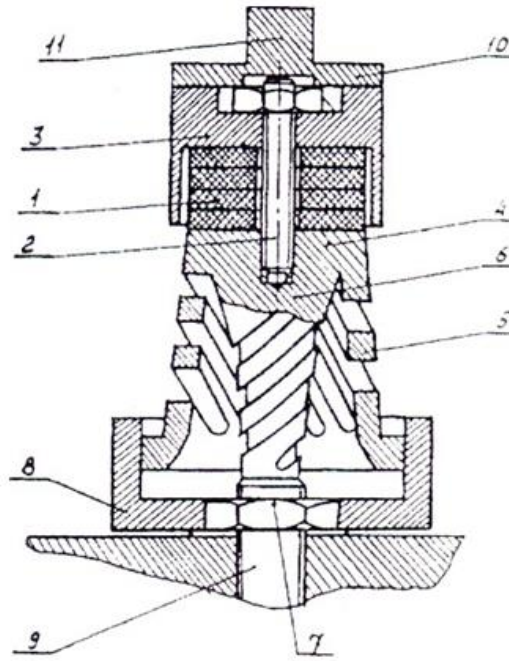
Спосіб розбирання різьбових з'єднань: 1 - п'єзокерамічний перетворювач; 2 - шпилька; 3- корпус; 4 – частотно-понижувальний елемент разом з торсіоном 5 і концентратором 6; 7- відгвинчувальна гайка; 8 - наконечник; 9- болт; 10, 11- перехідник і квадрат.
